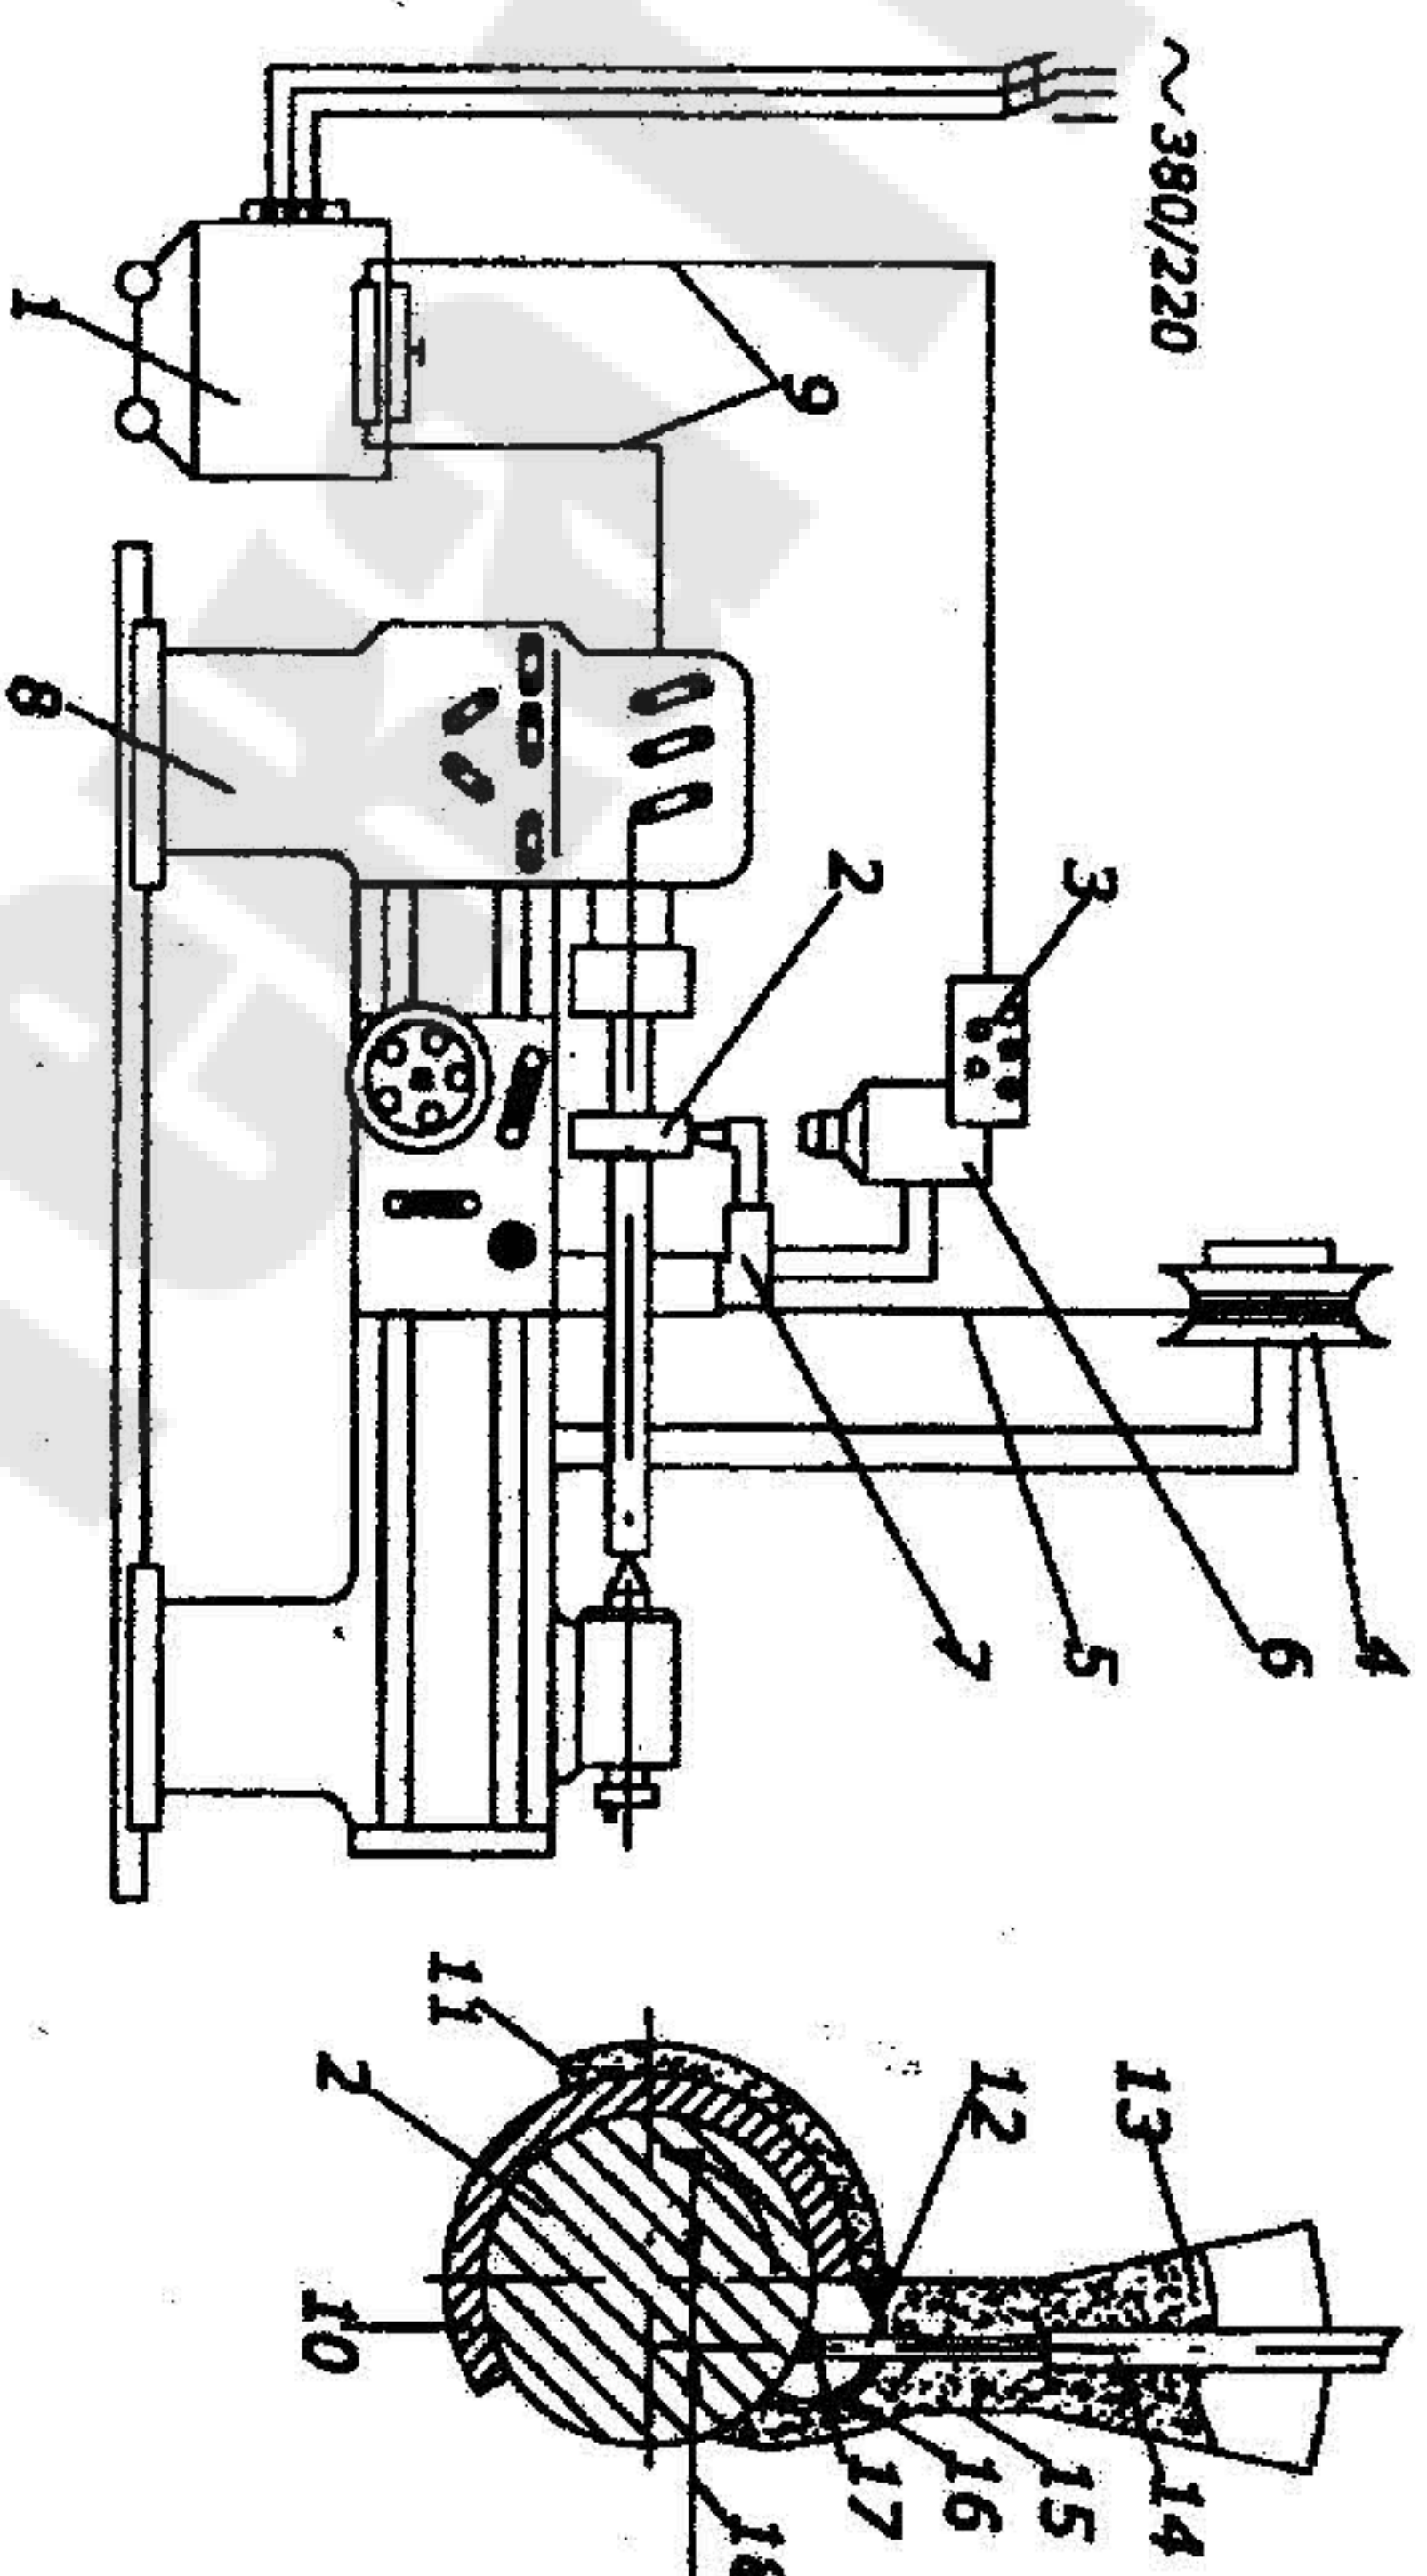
Схема установки для наплавки цилиндрических деталей под флюсом: 1 – сварочный выпрямитель ВС-600; 2 – наплавляемая деталь; 3 – пульт управления; 4 – кассета; 5 – электродная проволока; 6 – бункер с флюсом; 7 – сварочная головка; 8 – токарный станок; 9 – подвод сварочного тока; 10 – наплавленный металл; 11 – шлаковая корка; 12 – электродная проволока; 13 – бункер с флюсом; 14 – направляющий муштук; 15 – флюсовый муштук; 16 – обложка из жидкого флюса; 17 – сварочная дуга; 18 – смещение проволоки
